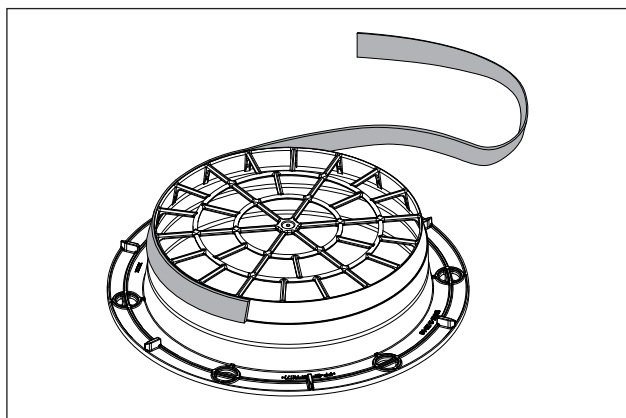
Position på forseglingsstapen til montering med rundrør
